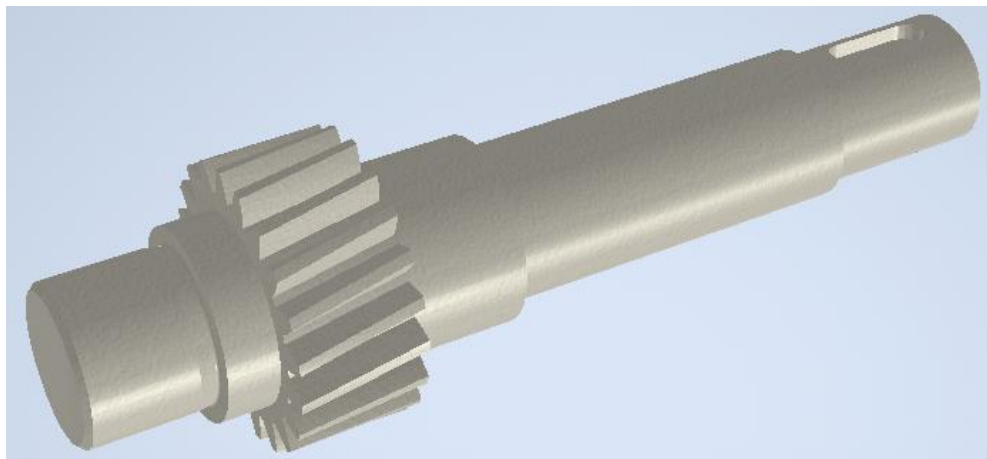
Вал-шестірня з циліндричною шестірнею
